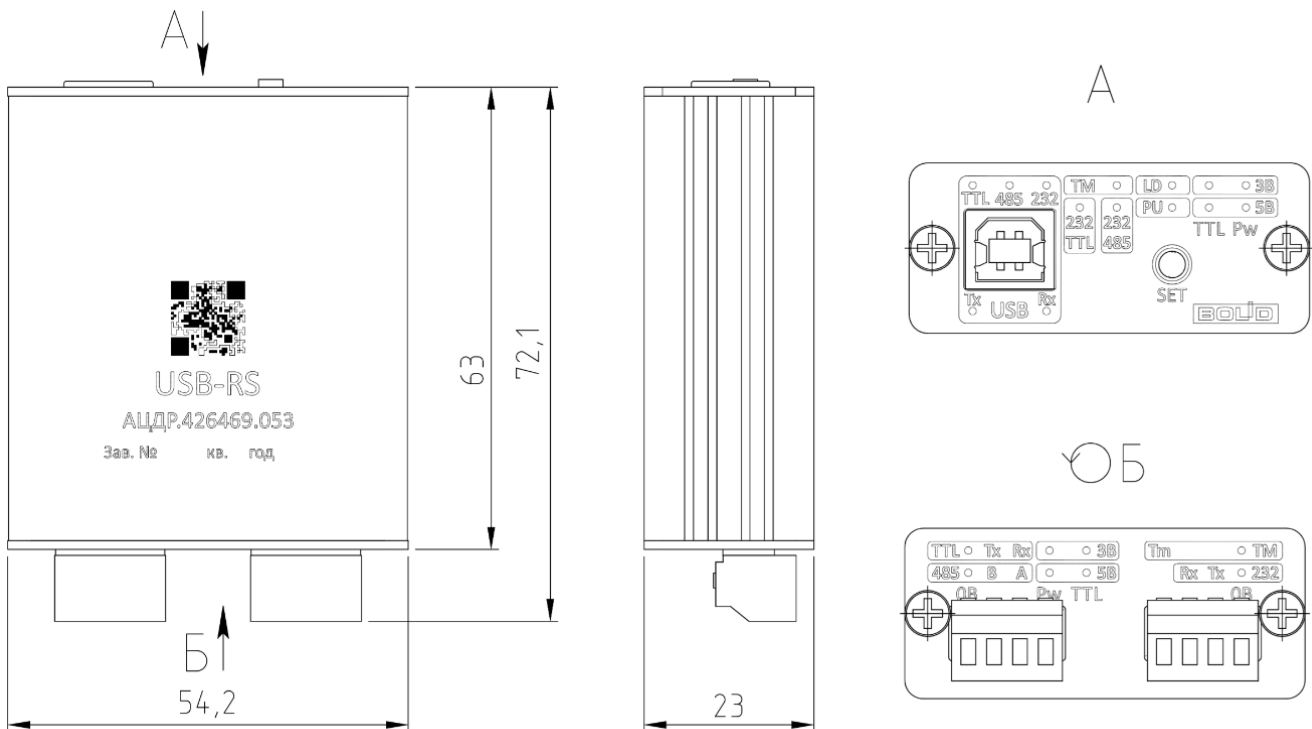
Внешний вид и габаритные размеры преобразователя «USB-RS»
